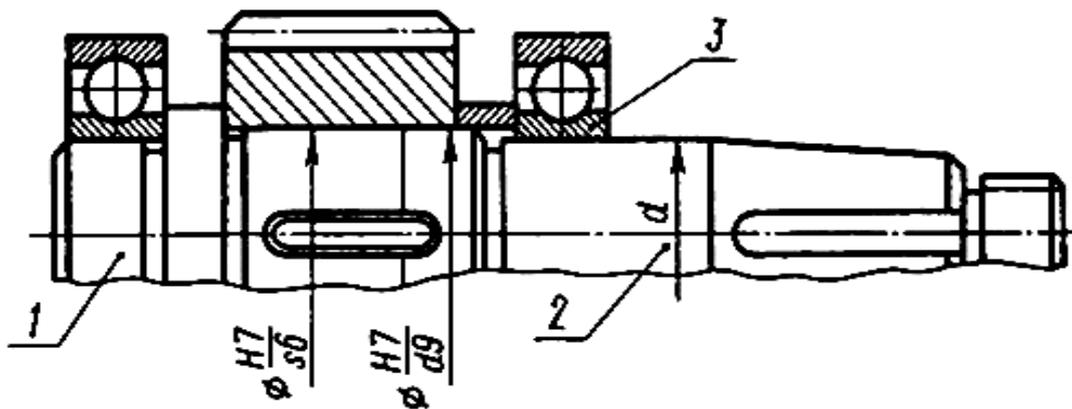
Прямой ступенчатый вал. 1- шип, 2- шейка, 3- подшипник.
